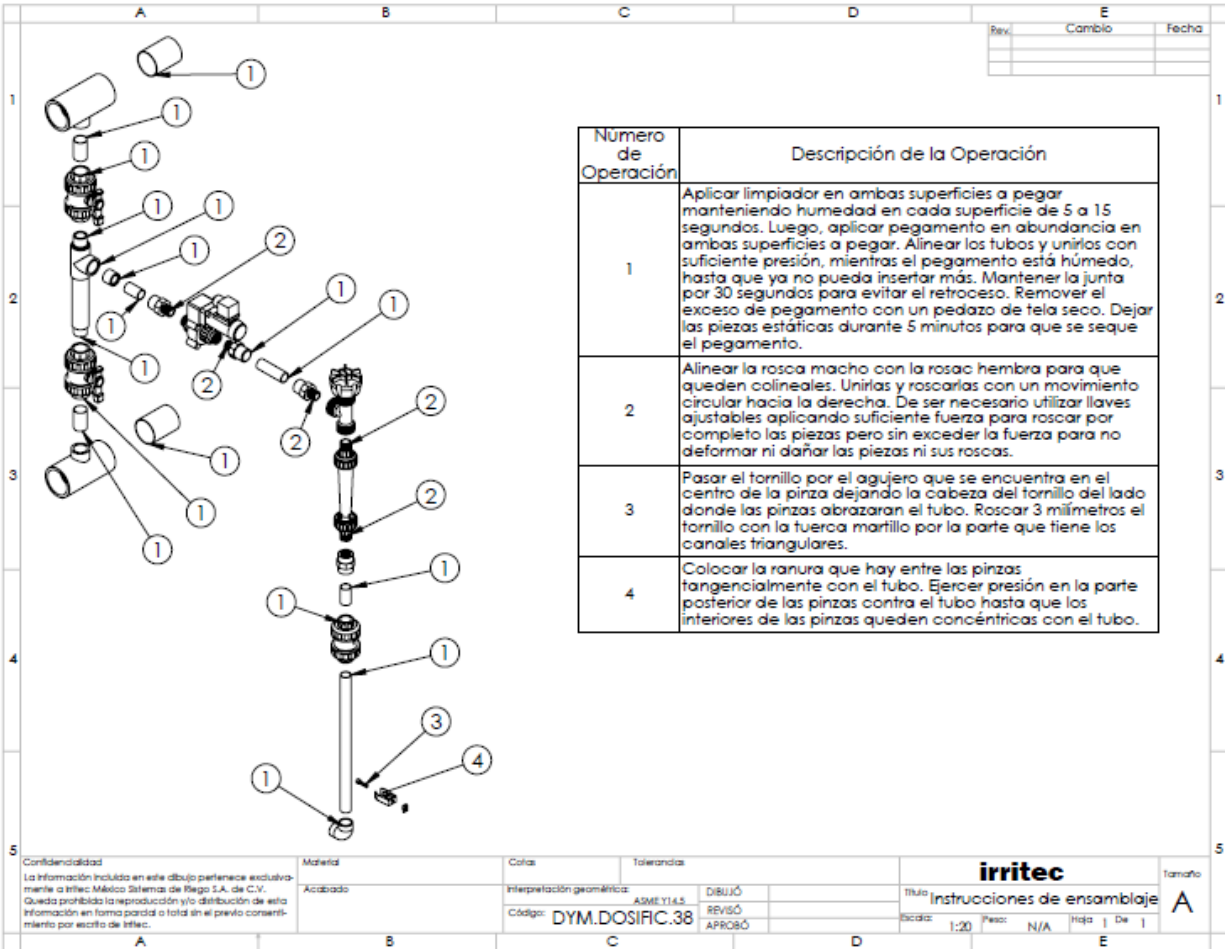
Plano de instrucciones de ensamblaje de sub-ensamblaje DYM.DOSIFIC.38.
